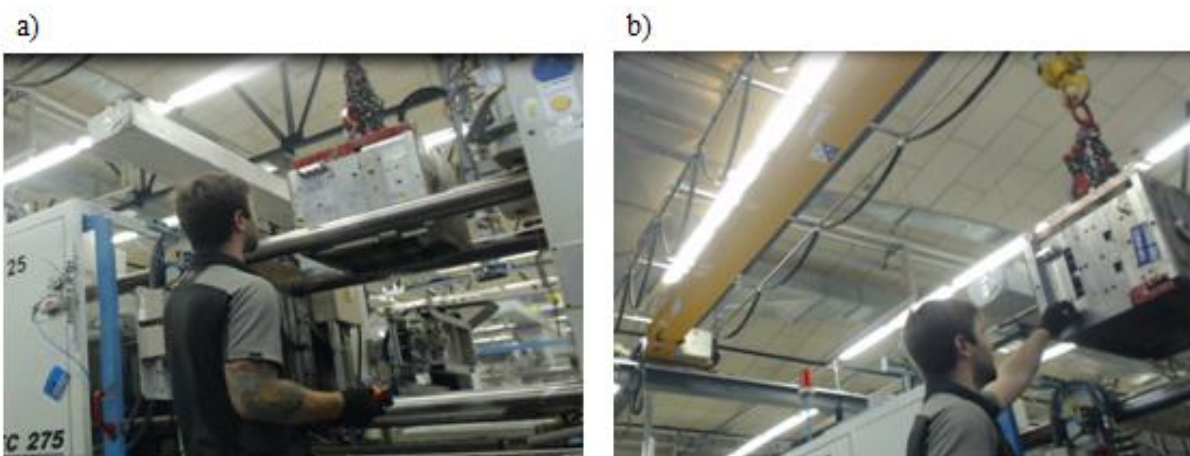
a) Retirar o molde da máquina; b) Colocar o molde na máquina com auxílio da ponte rolante
